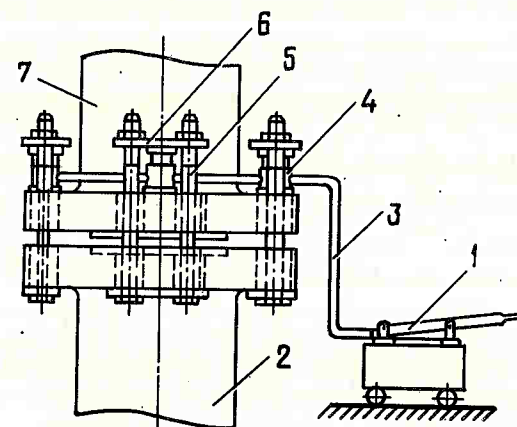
Подтягивание вала гидротурбины к валу гидрогенератора с помощью гидравлического приспособления:
